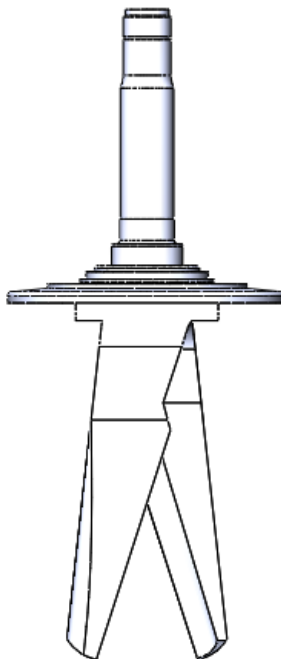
3d модель робочого органу ротаційного культиватора
